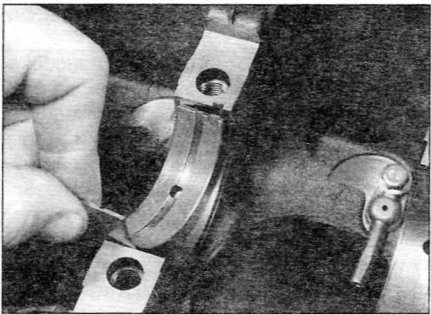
Снимите вкладыши верхних коренных подшипников с блока цилиндров/картера двигателя и уберите их на хранение вместе с нижними вкладышами
